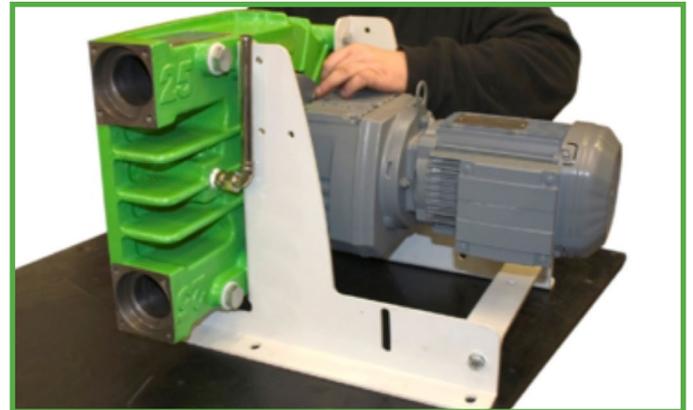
Montaggio del gruppo motore-riduttore (GMU)
